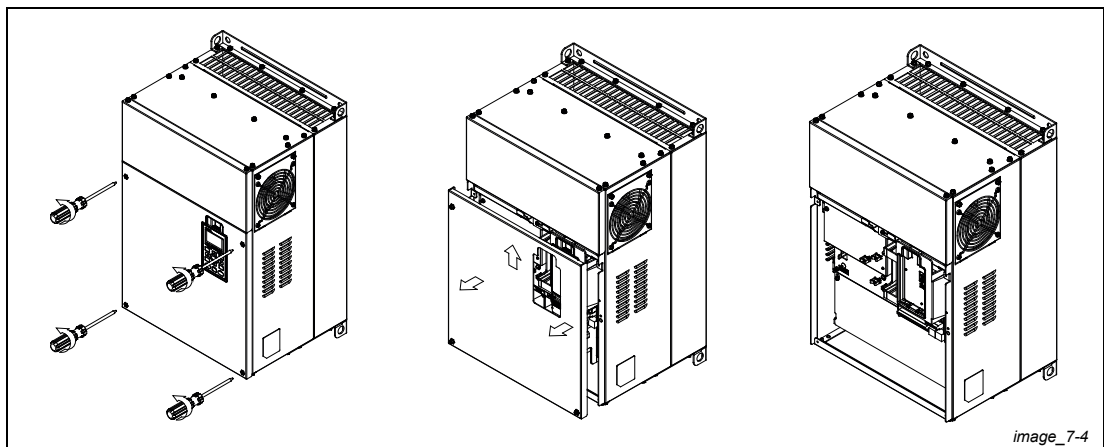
Entfernen der Frontabdeckung bei der Baugröße E
